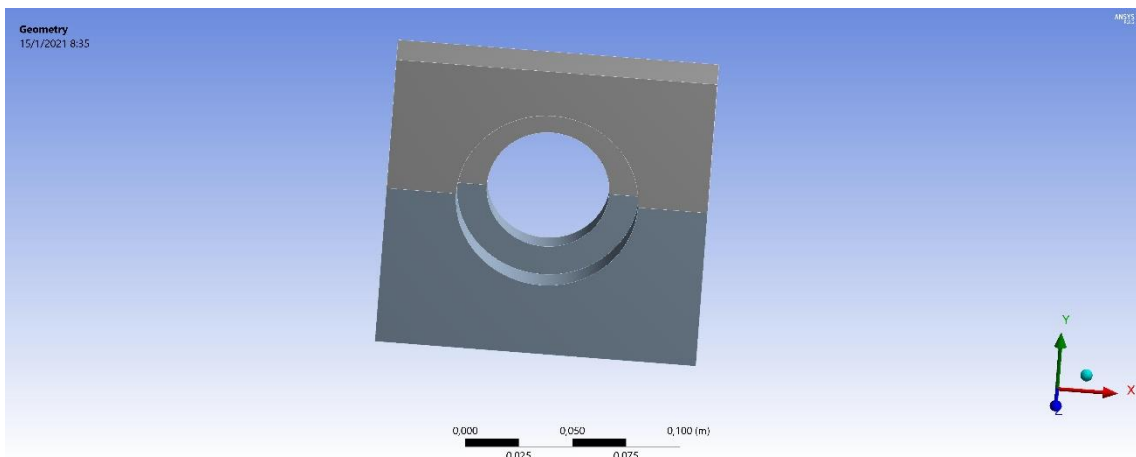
Definición de geometría - bastidor izquierdo de bobina
